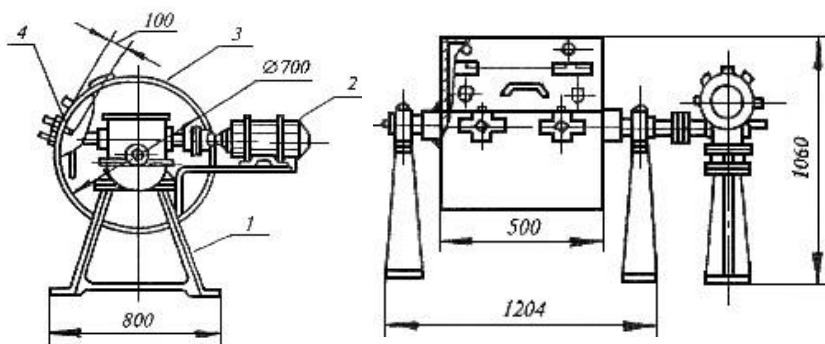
Полочный барабан: 1 - станина; 2 - двигатель; 3 - барабан; 4 - полка барабана
